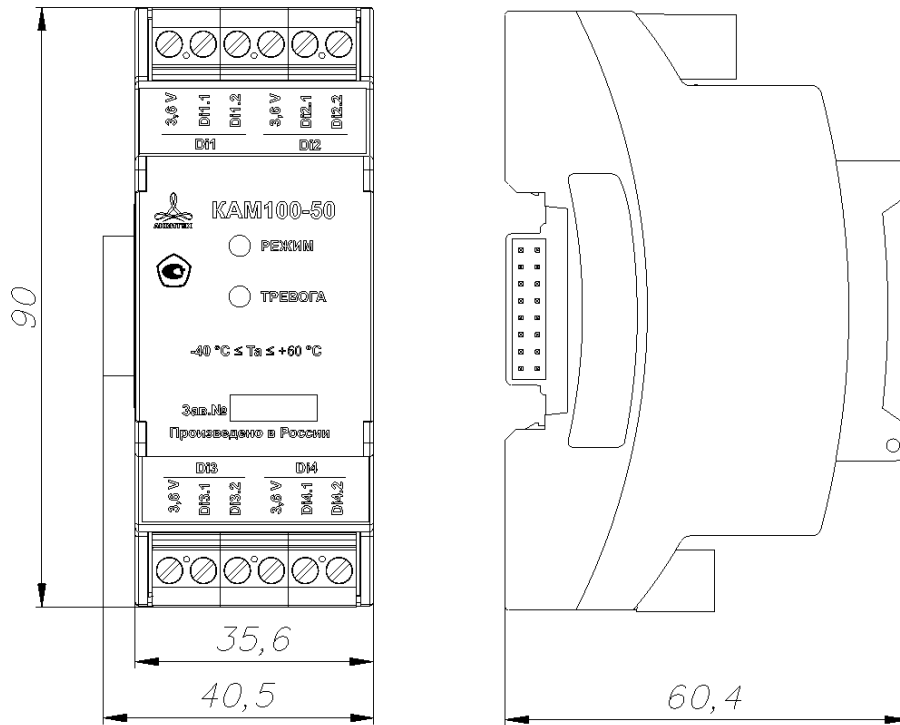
Внешний вид и габаритные размеры модуля дискретных входов KAM100-50
